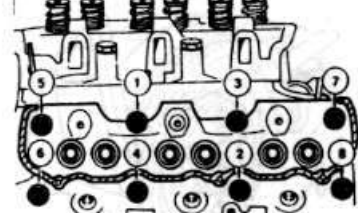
Последовательность затяжки болтов крепления головки цилиндров
